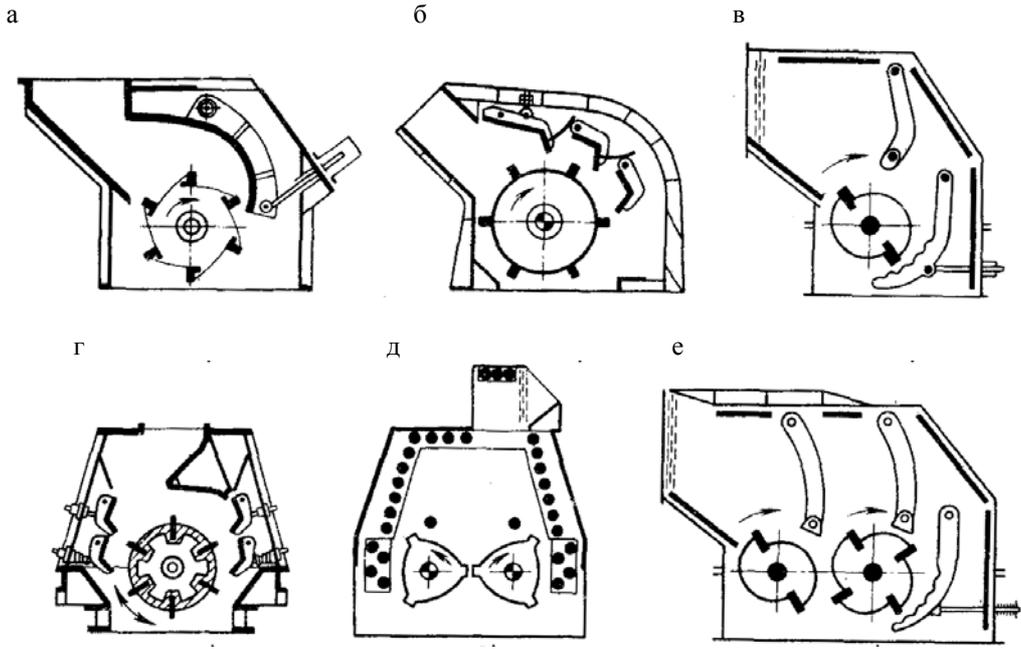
Схеми роторних роздрібноувачів: а – однороторний однокамерний з відбиваючою плитою; б – однороторний трикамерний з відбиваючими плитами; в – однороторний двокамерний з колосниковими решітками; г – реверсивний; д – двохроторний одноступінчастого подрібнення; е – двохроторний двоступінчастого подрібнення
